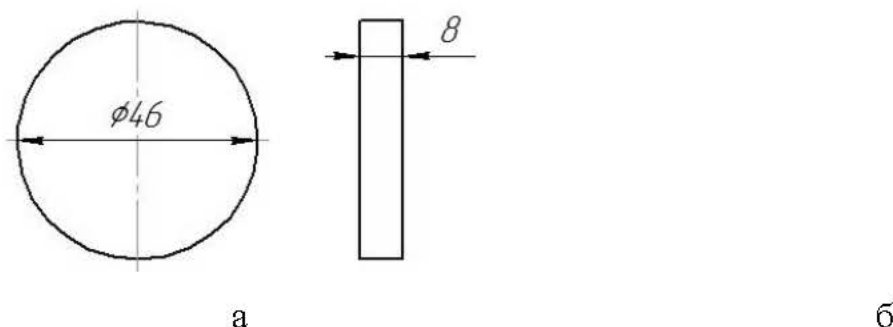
Зразки для вимірювання шорсткості поверхні
